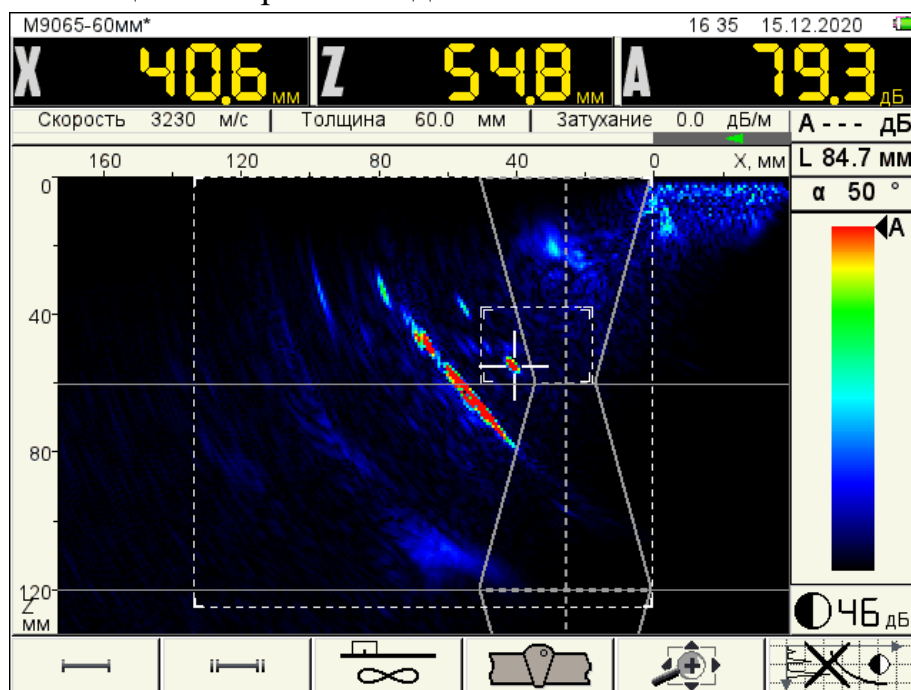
В-Скан при установленной зоне контроля и маске сварного шва
